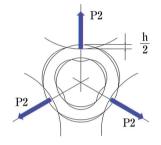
中空ワークの弾性反力の図 Fig. 2 Elastic reaction force of hollow workpiece
